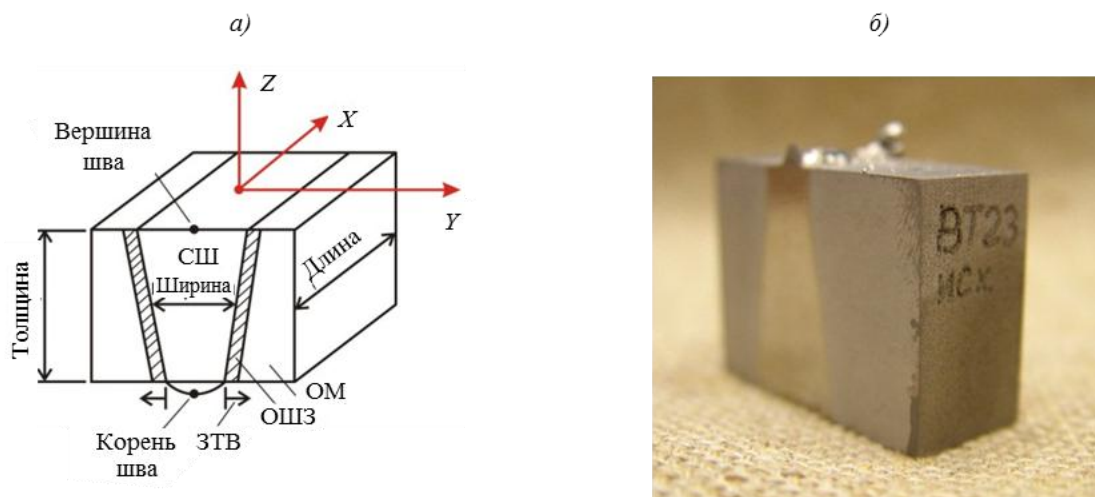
Схематическое изображение (а) и внешний вид (б) исследуемых образцов, вырезанных из плиты сплава ВТ23 после электронно-лучевой сварки:
